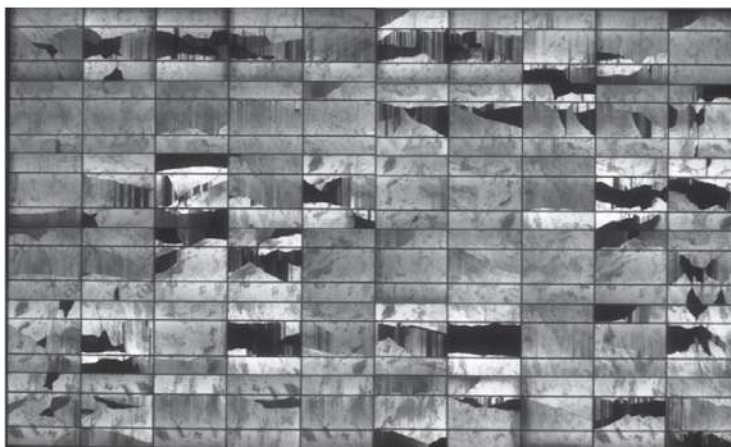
Panel con múltiples celdas que presentan grietas [37]
